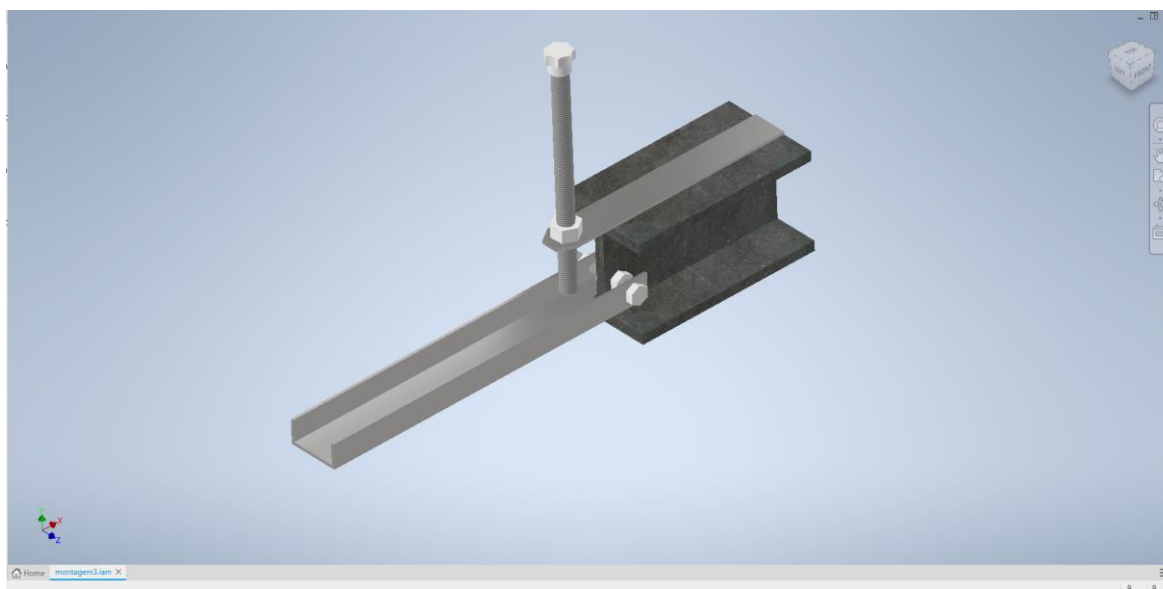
Desenho CAD da montagem das peças, in Autodesk Inventor.
